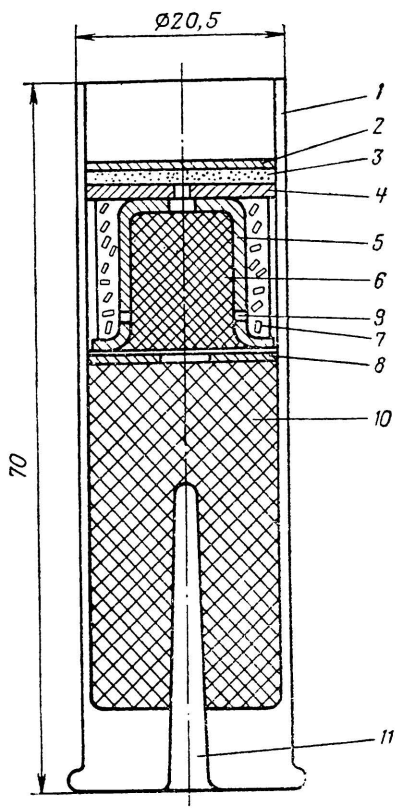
Модельный ракетный двигатель ДБ-51-С-10 с дымовой шашкой: 1 — корпус двигателя; 2 — дно двигателя; 3 — вышибной заряд (навеска); 4 — диафрагма замедлителя; 5 — корпус замедлителя; 6 — пиросостав замедлителя; 7 — гранулы цветного дыма; 8 — диафрагма пороховой шашки; 9 — отверстие для истечения дыма; 10 — пороховая шашка; 11 — сопло микро-РДТТ
